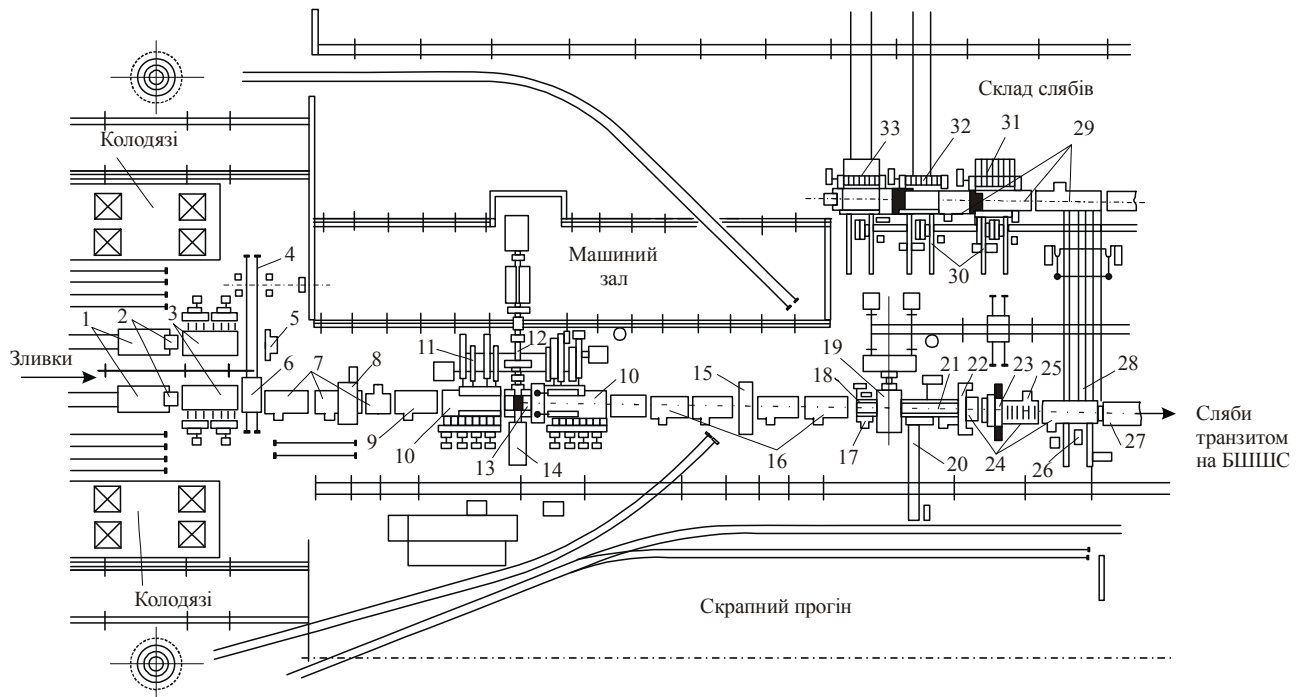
Схема розташування обладнання слябінга: 1 – зливковози, 2 – упор, 3 – приймаючий рольганг, 4 – рейковий шлях, 5 – стаціонарний упор, 6 – рольганг- візок, 7 – підвідні рольганги, 8 – терези, 9 – розкатний рольганг, 10 – робочі рольганги, 11 – маніпулятор з кантувачем 12 – шпинделі, 13 – універсальна кліть, 14 – машина перевалки валків, 15 – машина вогневої зачистки, 16,17, 21, 24, 29 – рольганги, 18 – зіштовхувачі, 19 – ножиці, 20 – транспортер обрізі, 22 – упор, 23 – клеймувач, 25 – терези, 26 – зіштовхувач, 27 – утопаючий упор, 28 – транспортер слябів, 30 – зіштовхувачі, 31 – стелажі, 32 – підйомний стіл, 33 – візок для слябів.
